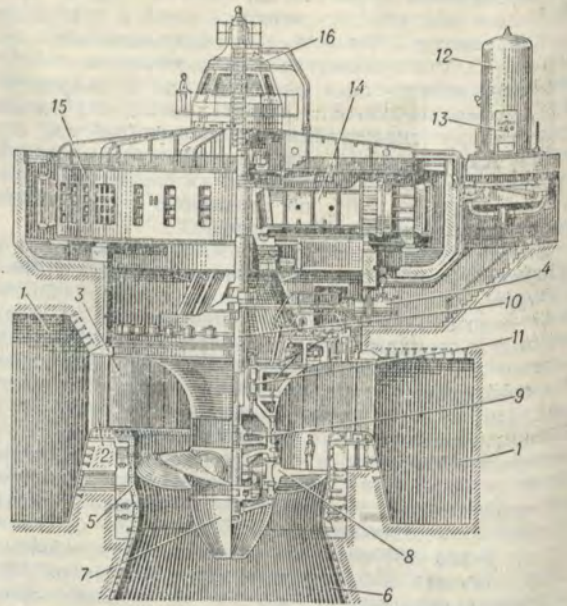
Разрез гидроагрегата: 1 — подводящая спиральная намера; 2 — статор турбины; 3 — лопатки направляющего аппарата; 4 — сервомотор направляющего аппарата; 5 — фундаментальная часть; 6 — отсасывающая труба; 7 — корпус рабочего колеса; 8 — лопатки рабочего колеса; 9 — сервомотор рабочего колеса; 10 — вал турбины; 11 — подшипник; 12 — масловоздушный напорный котел; 13 — колонна управления регулятора скорости; 14 — ротор генератора; 15 — статор генератора; 16 — воздухоподъемник.
